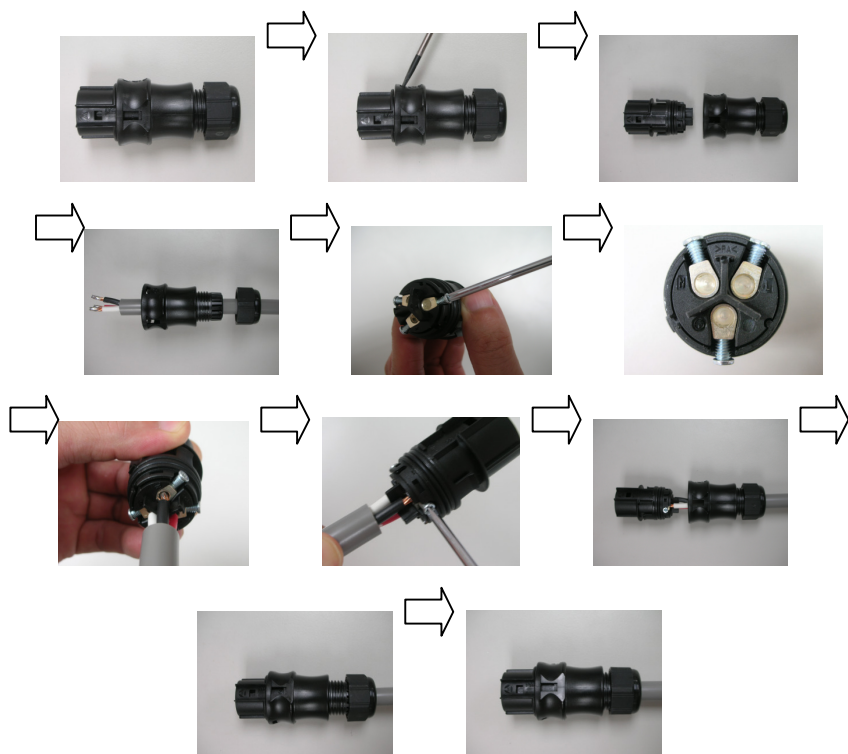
Assemblaggio del cavo e del connettore AC
